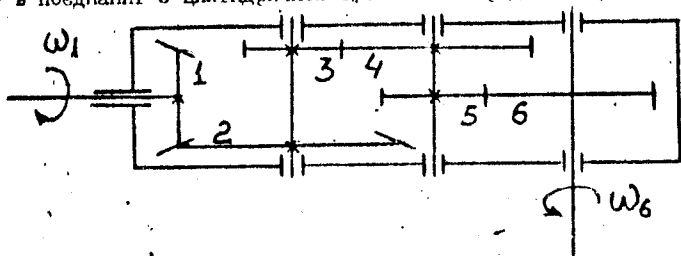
Схема конусно-циліндричного триступінчастого редуктора
